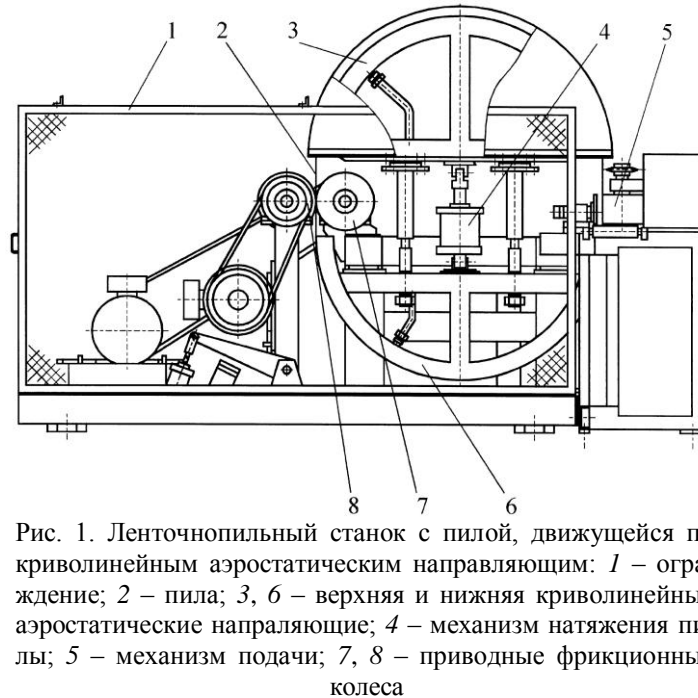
Ленточнопильный станок с пилой, движущейся по криволинейным аэростатическим направляющим: 1 – ограждение; 2 – пила; 3, 6 – верхняя и нижняя криволинейные аэростатические направляющие; 4 – механизм натяжения пилы; 5 – механизм подачи; 7, 8 – приводные фрикционные колеса
